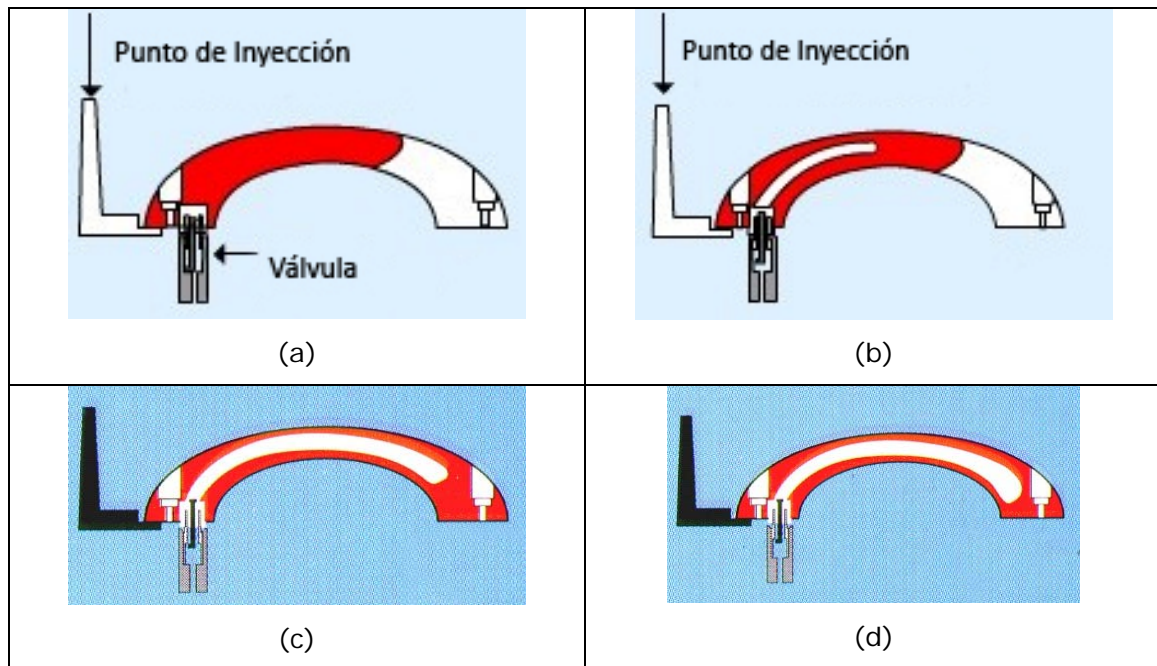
Etapas de la técnica de moldeo por inyección asistida por gas
